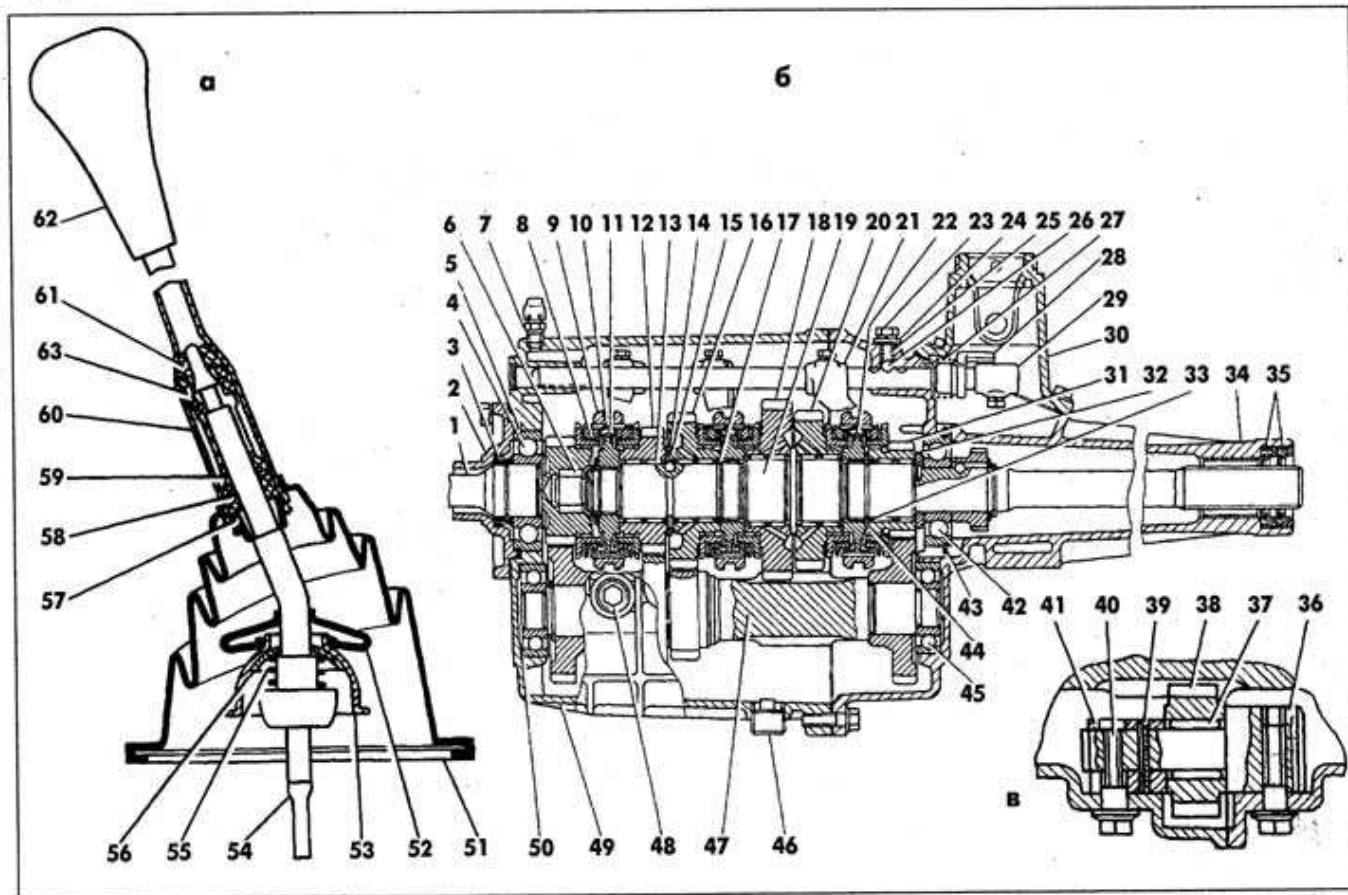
Коробка передач: а – рычаг переключения передач; б – продольный разрез; в – установка промежуточной шестерни заднего хода
